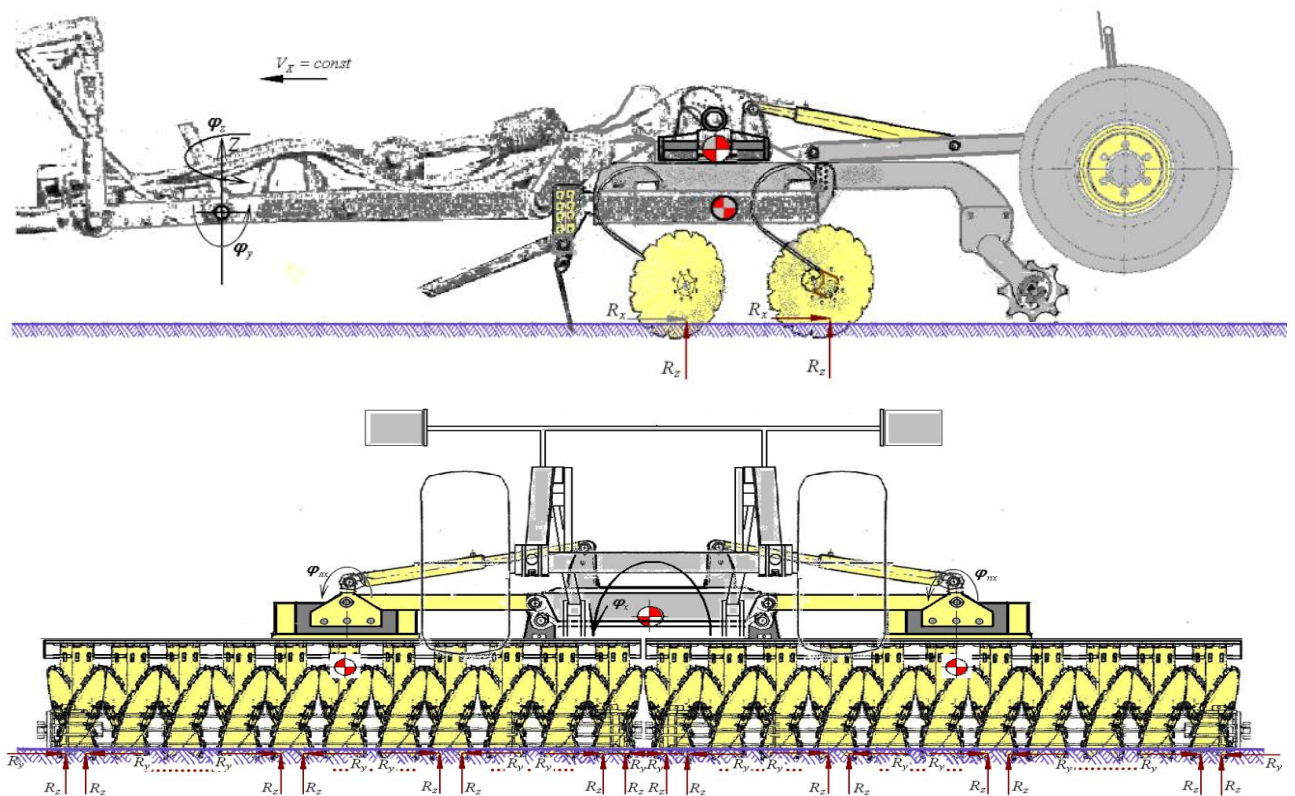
Схема конструкції дискатора в робочому режимі
